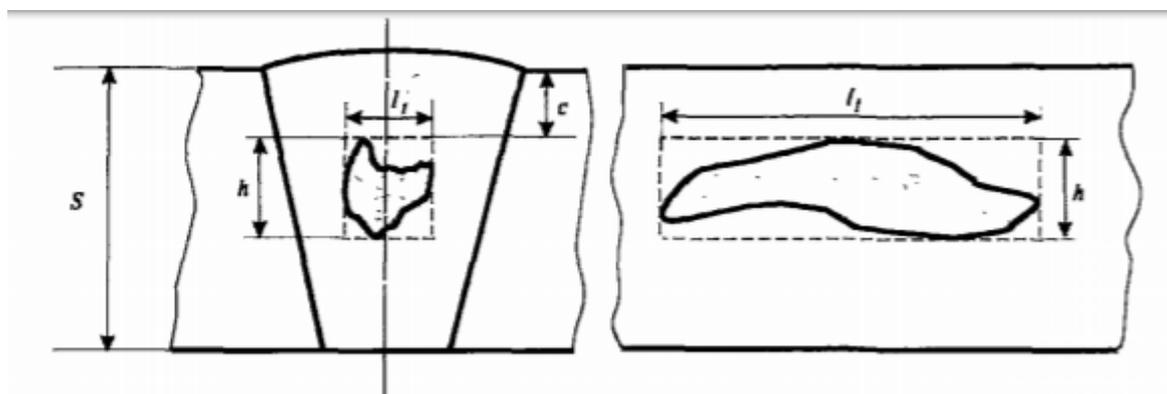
радиографический контроль сварных соединений [17]
